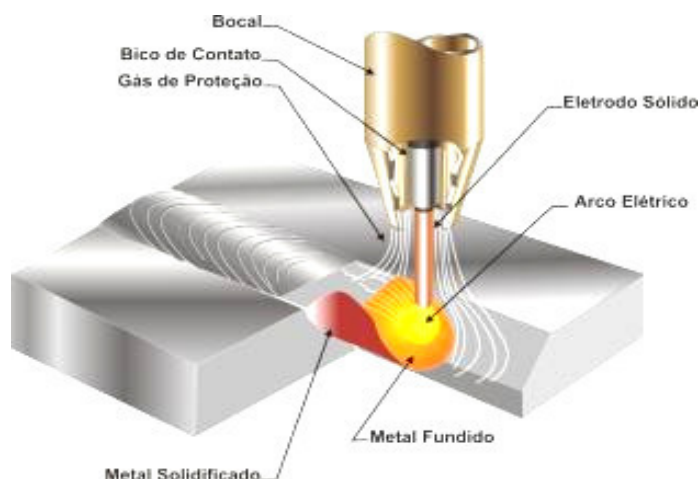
Descrição do processo de soldagem MIG (MARQUES *et al.*, 2009).
